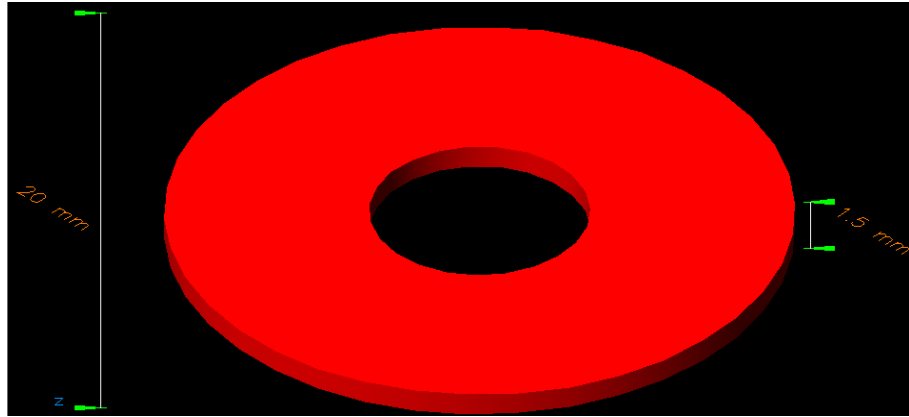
Soportes para el embobinado diseñado en Mechanical Desktop
